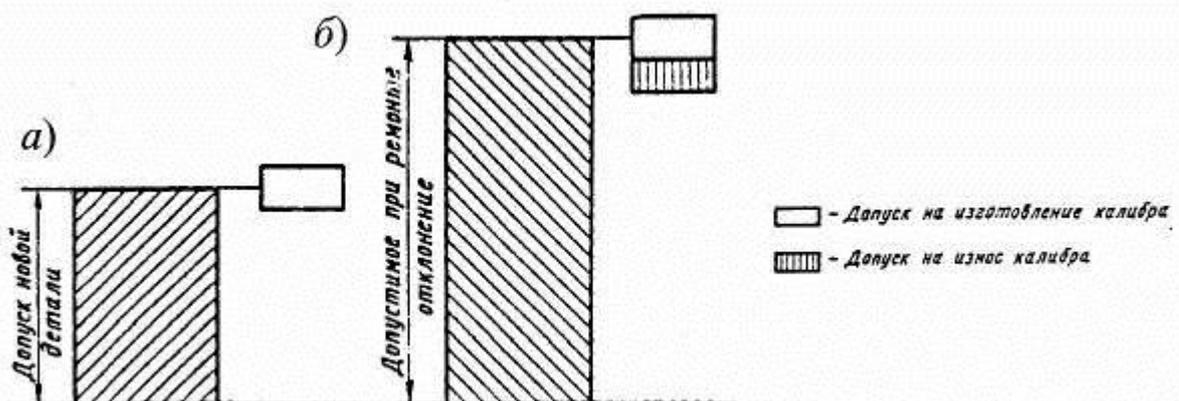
Схема полей допусков калибров: а — рабочий проходной калибр; б — дефектовочный калибр
